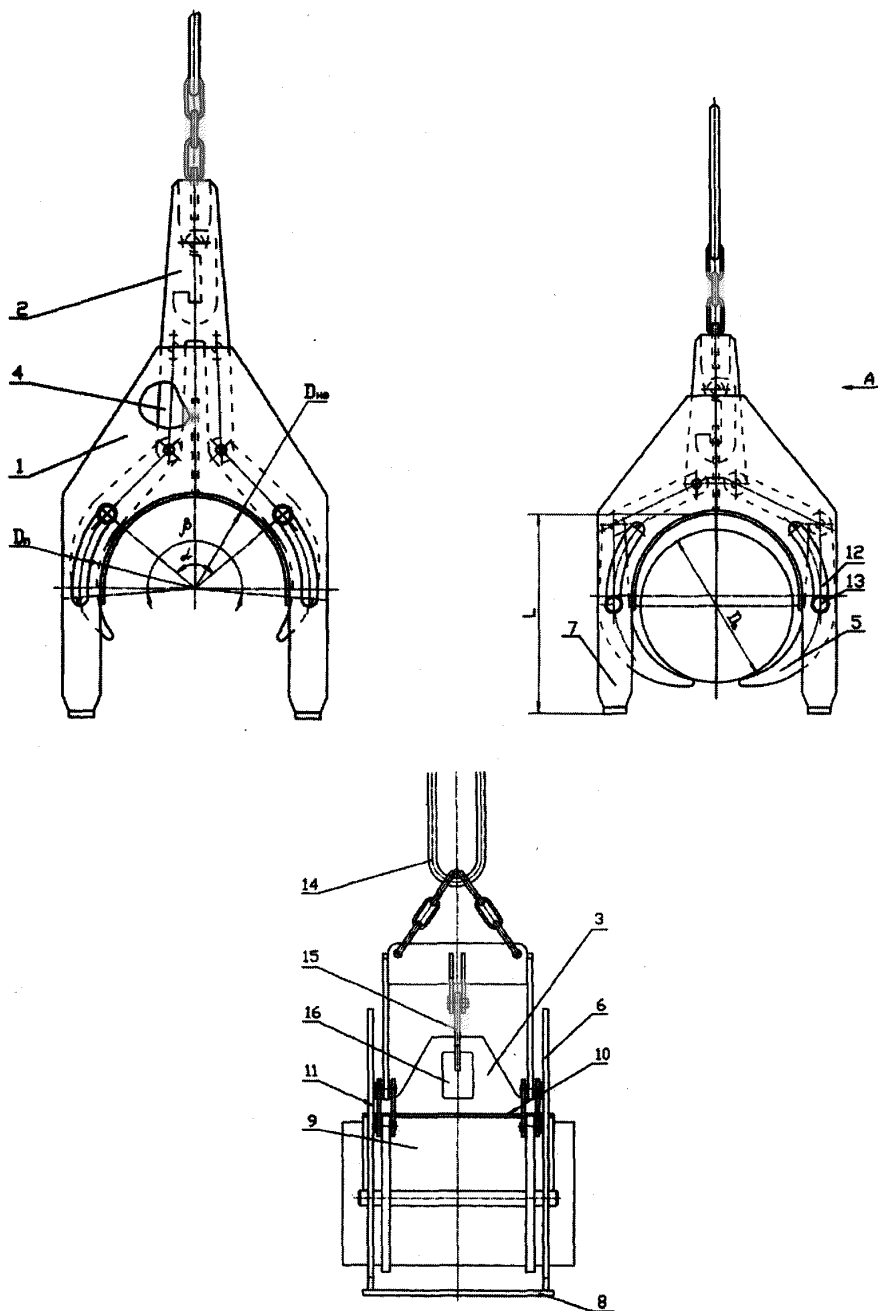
Захватний пристрій для циліндричних вантажів.
